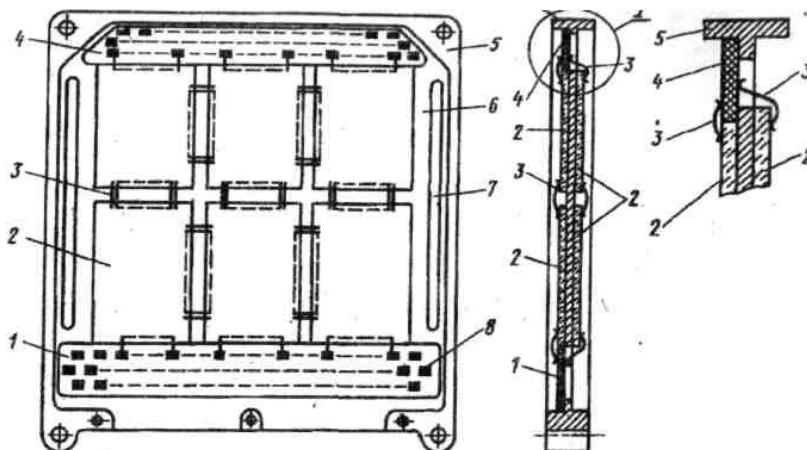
Конструкция двухсторонней ФЯ на металлической рамке:
